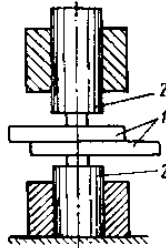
Схема сварки без предварительного зажатия свариваемых деталей.
